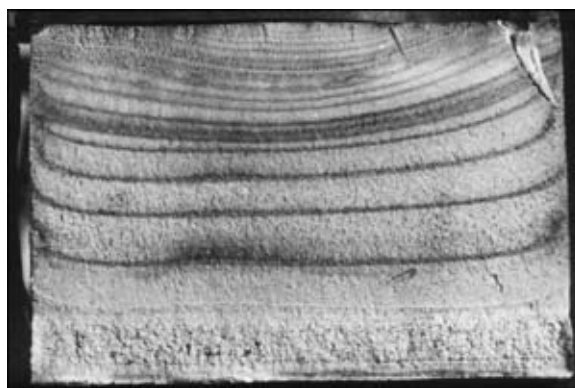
Вид усталостного излома образца таврового сварного соединения с индикаторными следами кинетики роста поверхностной полуэллиптической трещины
